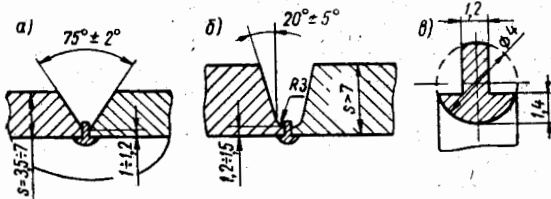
Конструктивные элементы подготовки кромок стыковых соединений труб из стали X18H10T, 0X18H12B и X17H13M2T, выполняемых ручной аргонодуговой сваркой с расходными вставками (по ОН 26-01-71-68): а — V-образная разделка кромок; б — V-образная разделка кромок с криволинейным скосом; в — профиль расходного кольца
